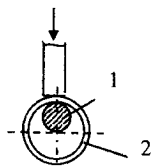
Схема розкочування: 1 – циліндрична оправка; 2 – деталь.
